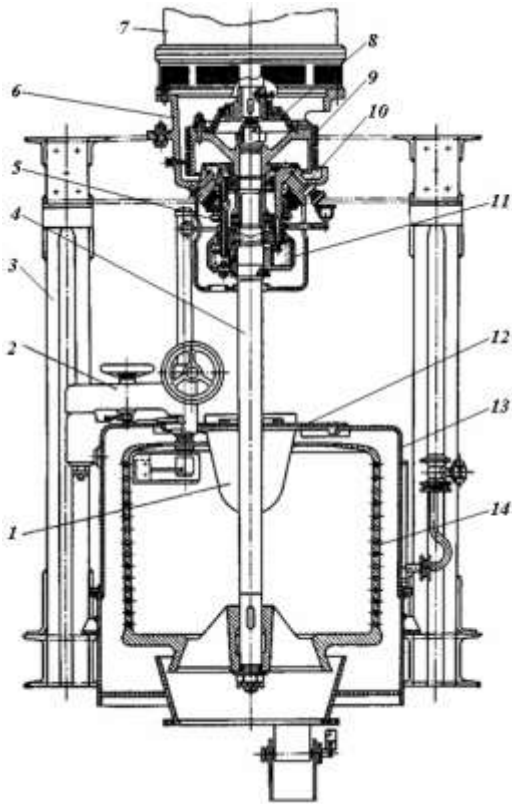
Загальний вигляд центрифуги та привод механізму
